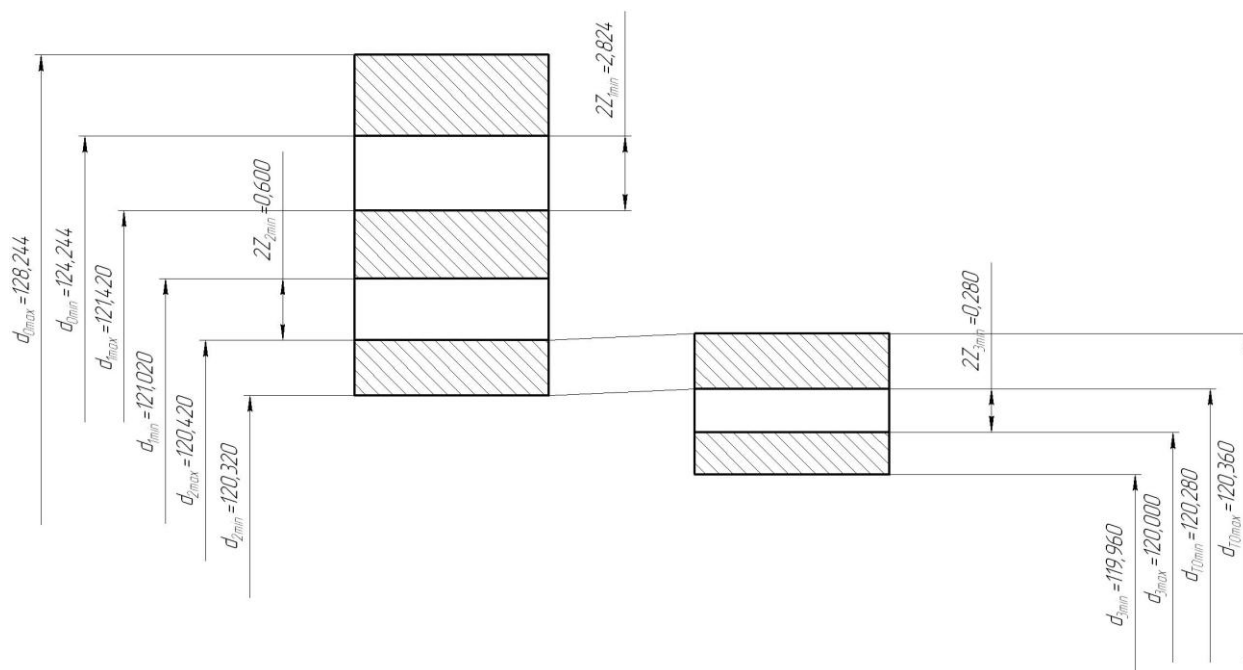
Схема расположения припусков и полей допусков на поверхность $\varnothing 125h7(-0,04)$.
